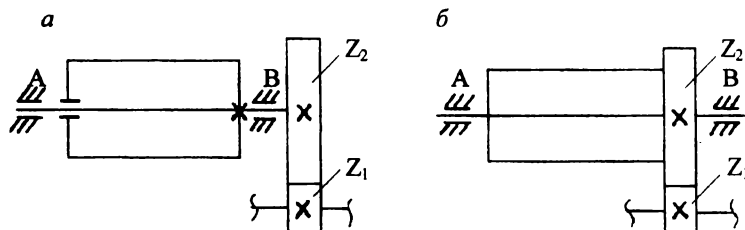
Схема установки барабана с открытой зубчатой передачей:
